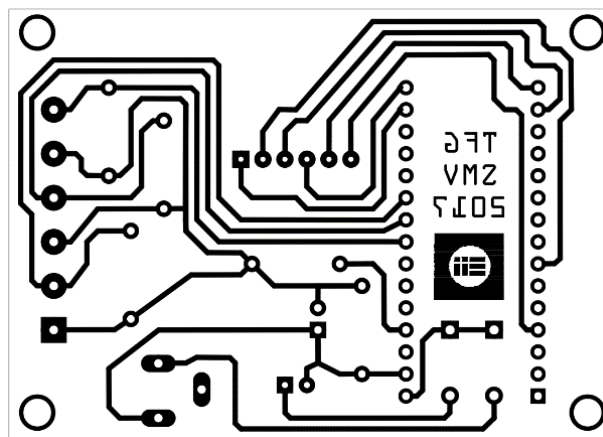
Fitolito de cara de soldadura de PCB.
